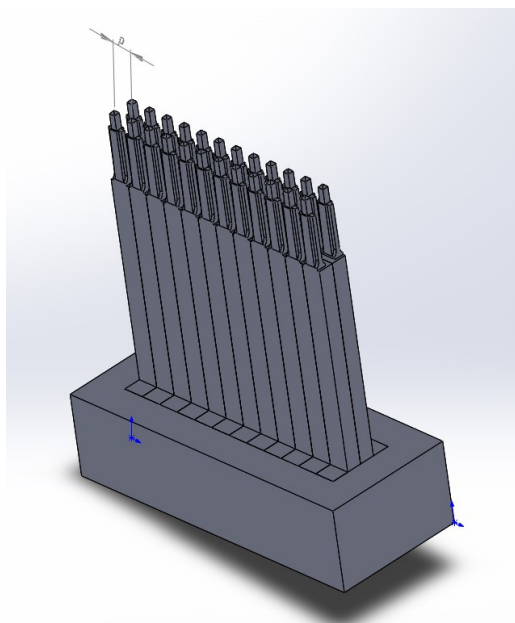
Сборная конструкция формообразующих элементов пресс-формы
